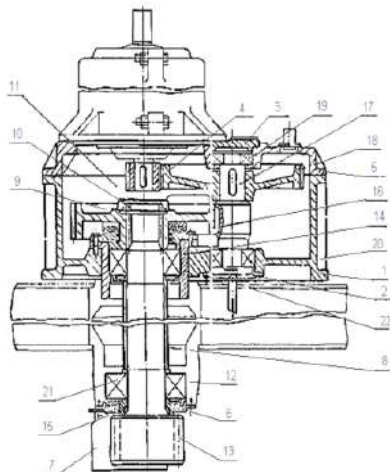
, 6 . Редуктор поворота ЭКГ-10: 1 – корпус редуктора; 2 – крышка; 3 – крышка; 4 – шестерня ведущая ($z=23, m=8$); 5 – крышка редуктора, 6 – половина; 7 – кожух; 8 – труба распорная; 9 – шпонка; 10 – Гайка (М 160x4) 11 – крышка; 12 – крышка сквозная; 13 – вал-шестерня; 14 – стакан; 15 – манжета; 16 – колесо зубчатое ($z=70, m=12$); 17 – вал-шестерня ($z=12, m=14$); 18 – колесо зубчатое ($z=103, m=8$); 19 – роликоподшипник №3622; 20 – роликоподшипник №3626; 21 – роликоподшипник №3644; 22 – роликоподшипник №3640; 23 – кольцо 292*16
